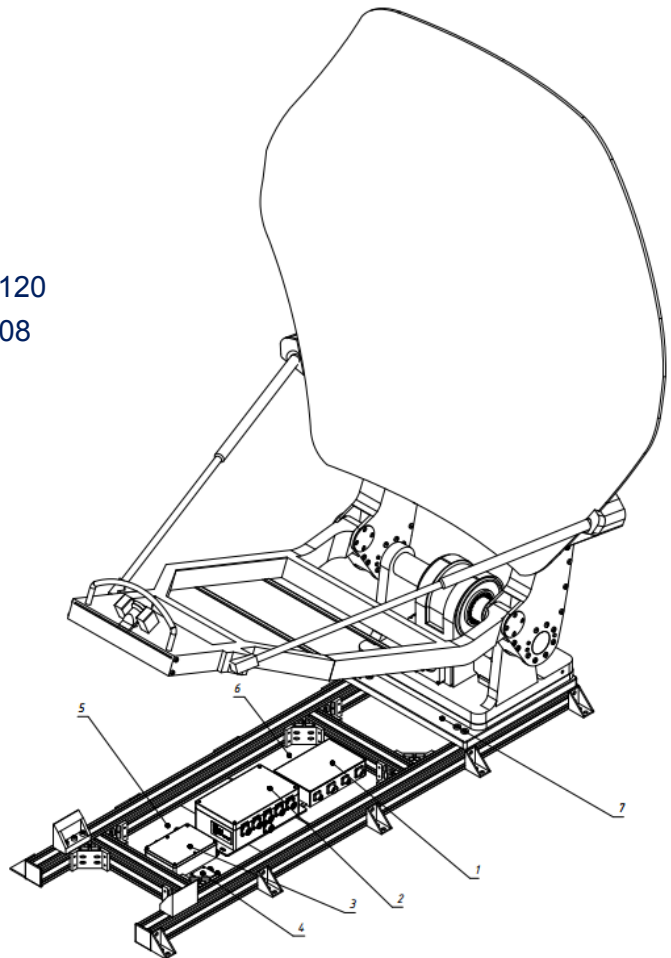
Размещение основного оборудования СНА на переходной раме ОПУ антенной системы ППК SNG 1,5 м
